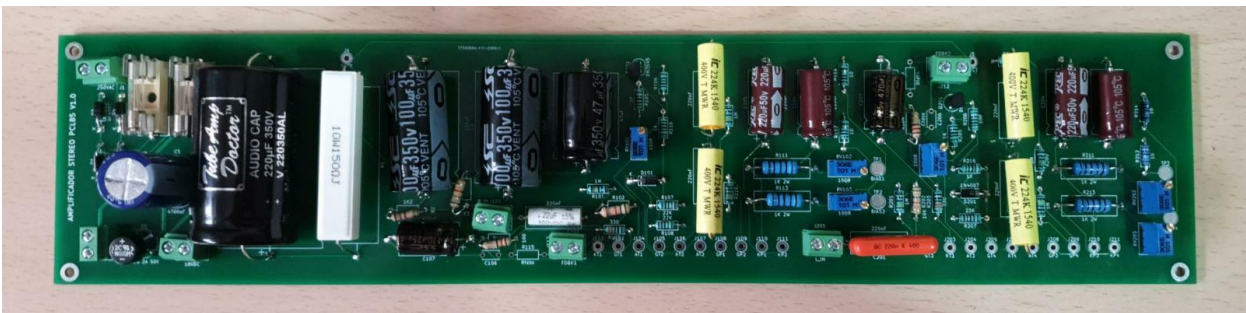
PCB con todos sus componentes soldados.
